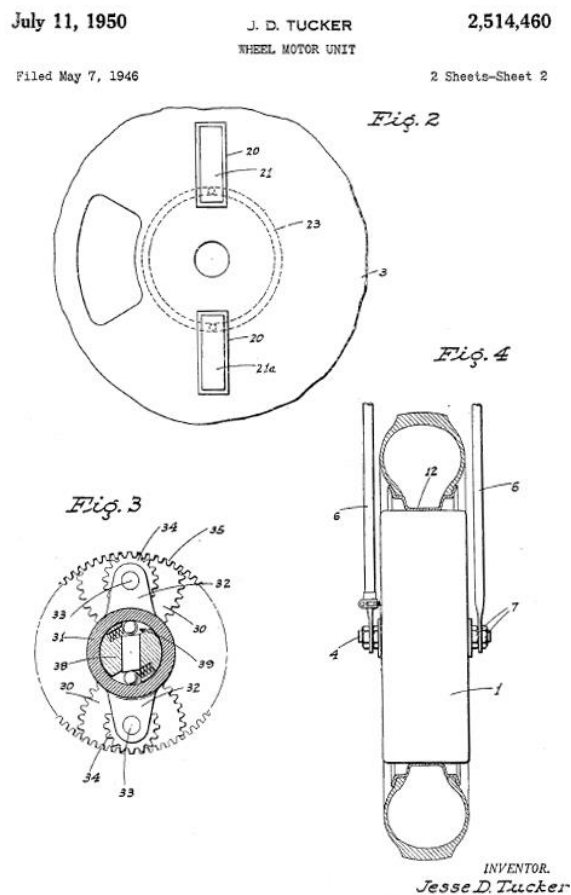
Зображення прототипа усіх редукторних «мотор колес»
